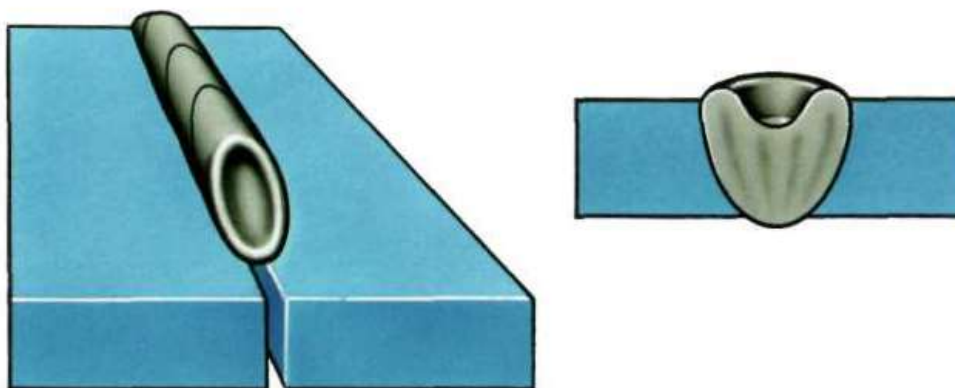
Дефект сварного шва по типу усадочной раковины
